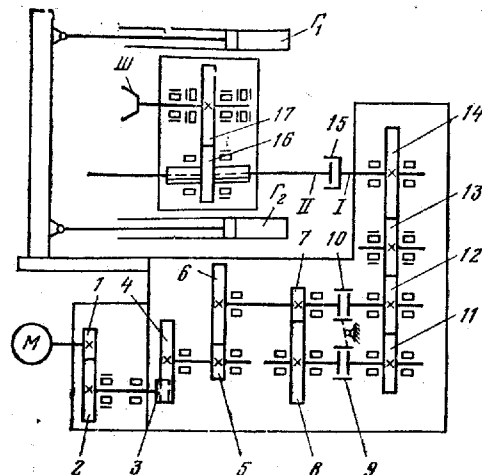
Гидрокинематическая схема бурового станка Б68КП
